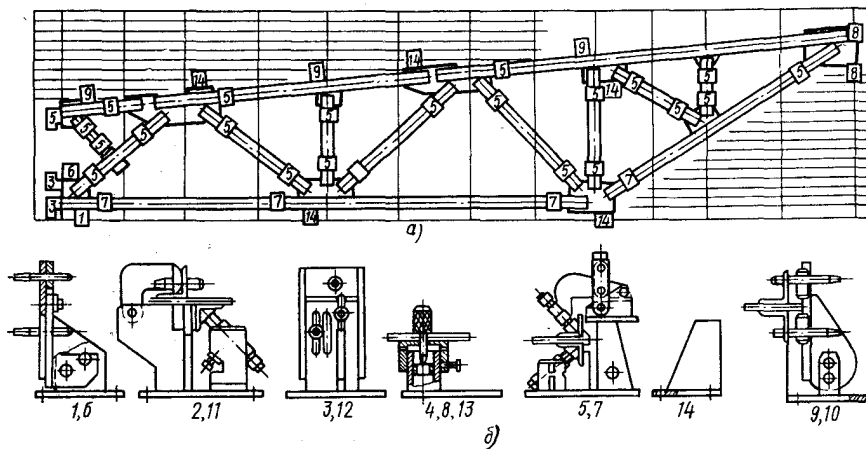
Кондуктор для ферм с применением универсальных сборочных приспособлений
